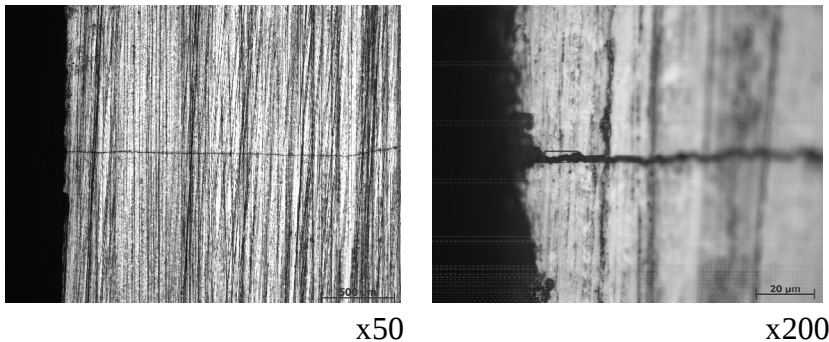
Загальний вид передніх поверхонь твердого сплаву марки VK8 після заточування колами з карбіду кремнію
